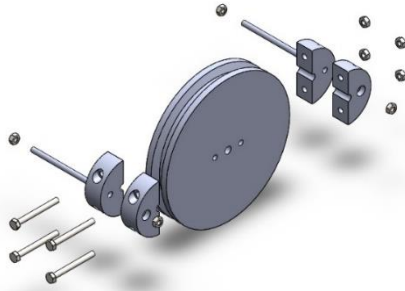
Vista explosionada polea 2. Fuente: Propia.
